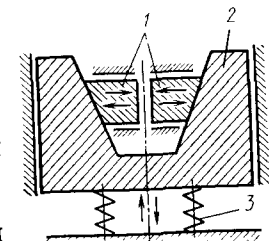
Схема самоцентрирующего приспособления для зажима иглы: 1 — пружина; 2 — призма; 3 — зажимные губки
